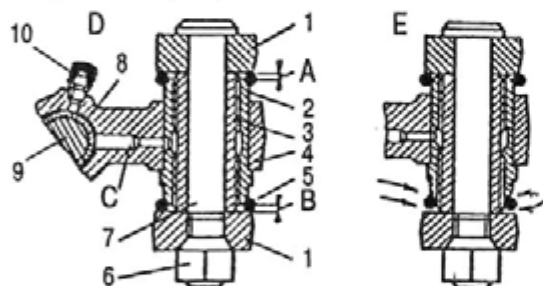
Шарнирное соединение нижнего конца стойки: 1 - головки рычагов передней подвески; 2 - наружная резьбовая втулка; 3 - распорная резьбовая втулка; 4 - головка стойки передней подвески; 5 - защитное кольцо; 6 - гайка; 7 - палец; 8 - игольчатый подшипник; 9 - шкворень; 10 - масленка; С - масляный канал, D - рабочее положение втулки 2; E - сдвинутое ненормальное положение втулки 2.
